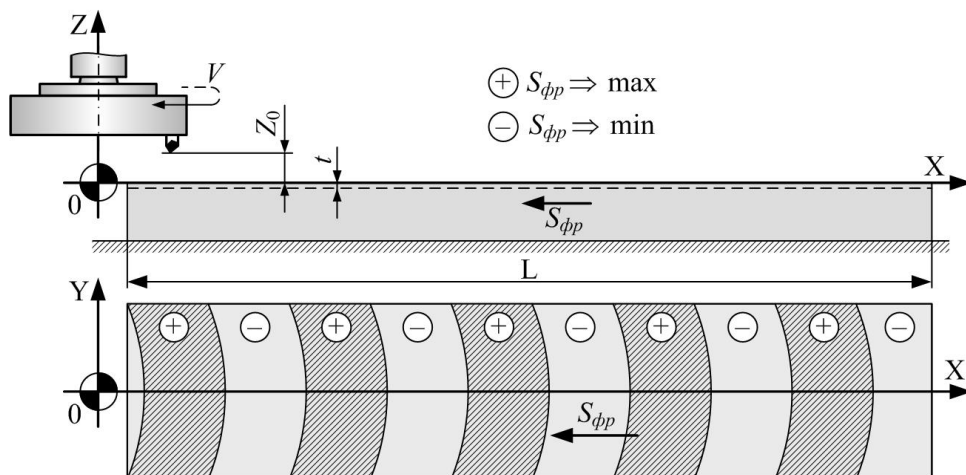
Схем торцевого фрезерования композитом 10 плоской поверхности заготовки с дискретным изменением величины подачи $S_{фр}$ на станке с ЧПУ
